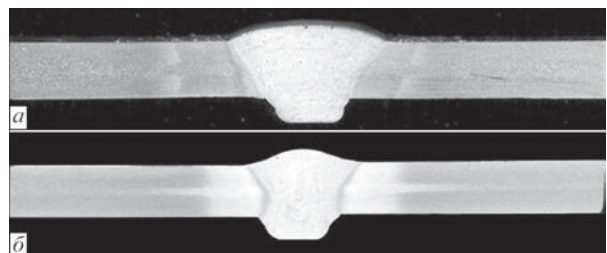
Внешний вид макрошлифов сварных соединений пластин из сплава 1561: а — дуговая сварка; б — гибридная плазменно-дуговая сварка
